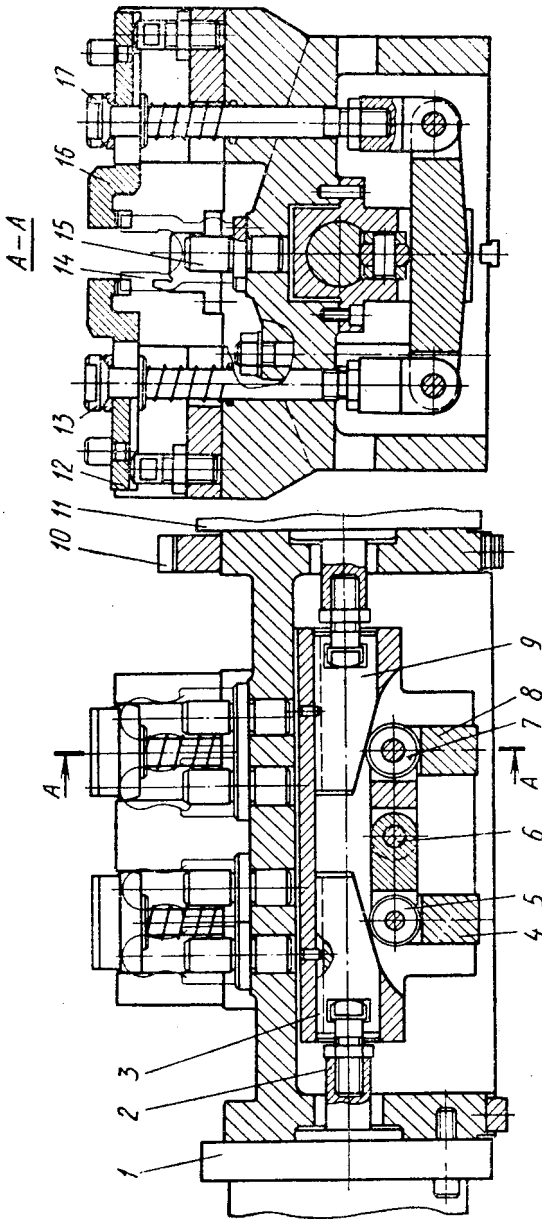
Многоместное приспособление для фрезерования внутренних плоскостей вилок
